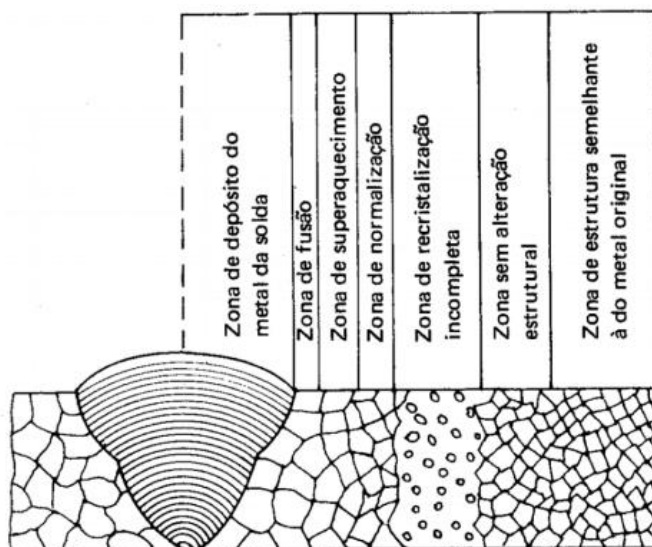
Representação esquemática dos fenómenos metalúrgicos que ocorrem durante a soldadura [16]
